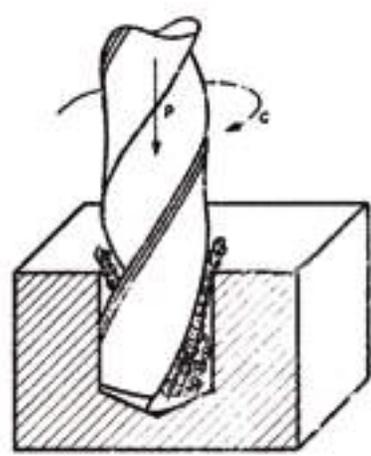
Movimento de corte (c) e de penetração (p) na furação.
